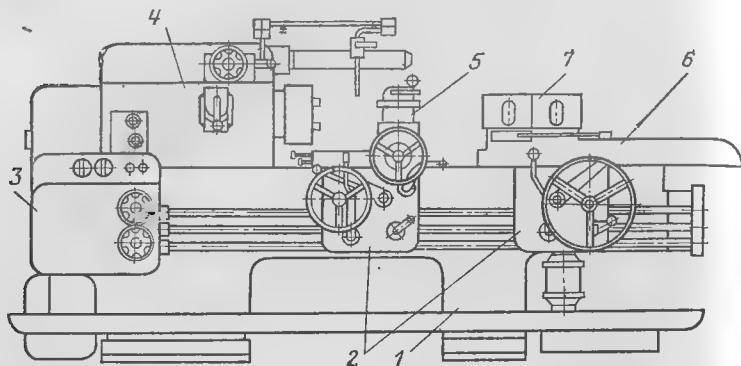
Общий вид токарно-револьверного станка модели 1П365.
